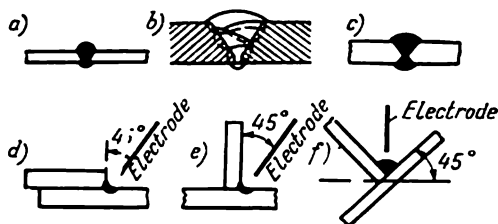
Schémas de l'exécution des cordons de soudure en bout et d'angle
